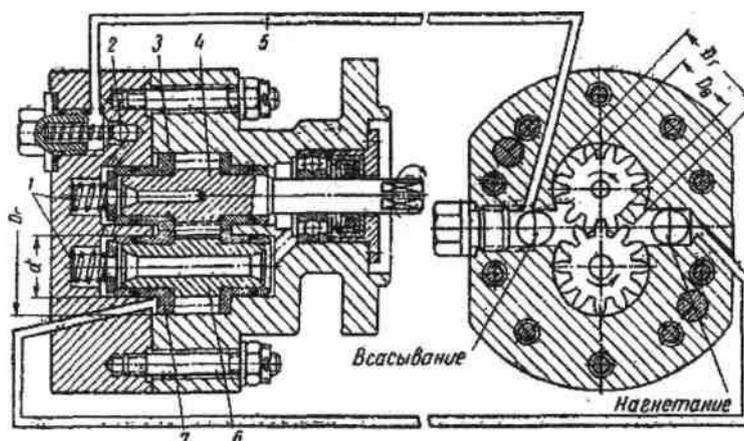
Схема насоса с плавающими торцовыми втулками
